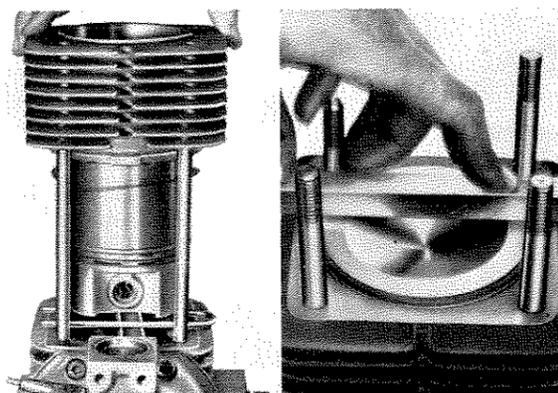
Montaggio cilindro e controllo altezza pistone
